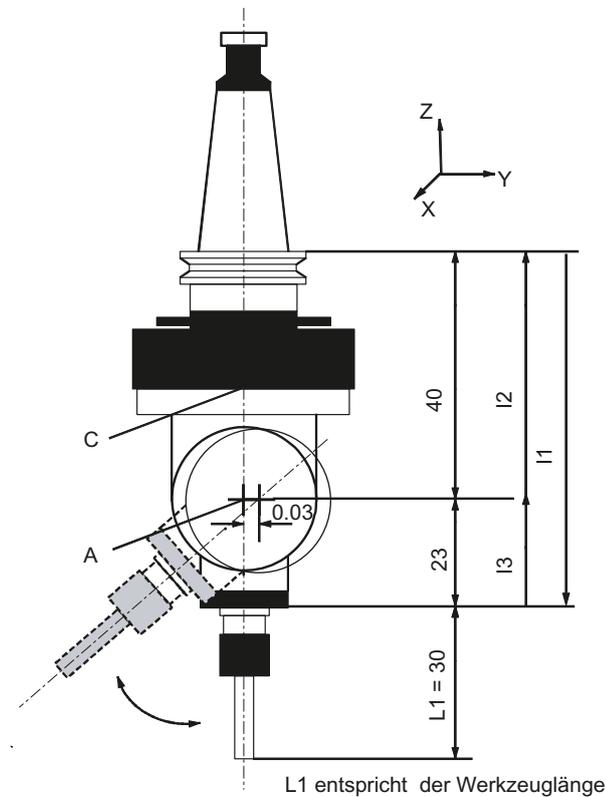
Schwenkkopf 1 "HEAD\_1"
